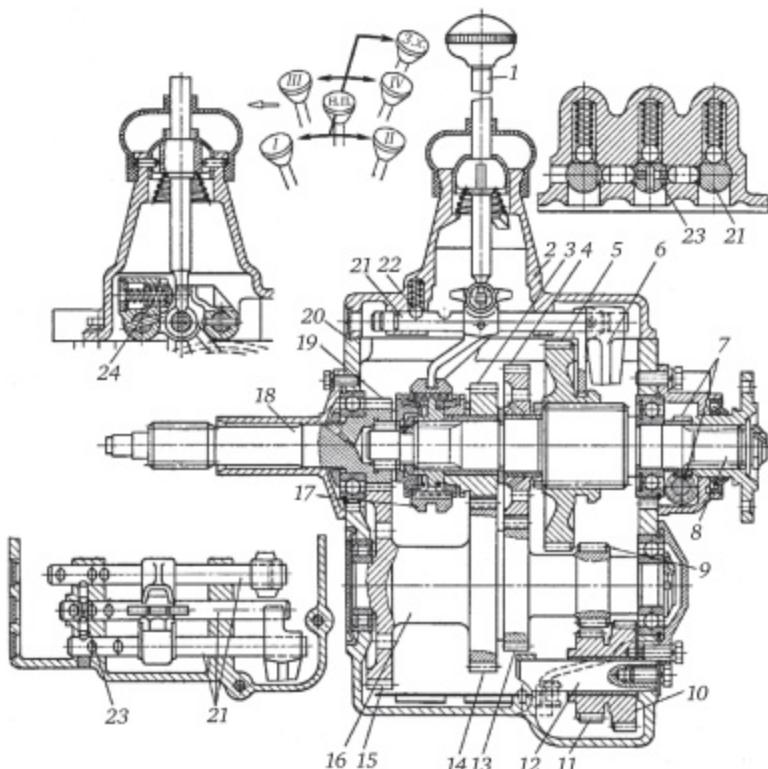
Конструкция 3-вальной 4-ступенчатой коробки передач грузового автомобиля классической компоновки
